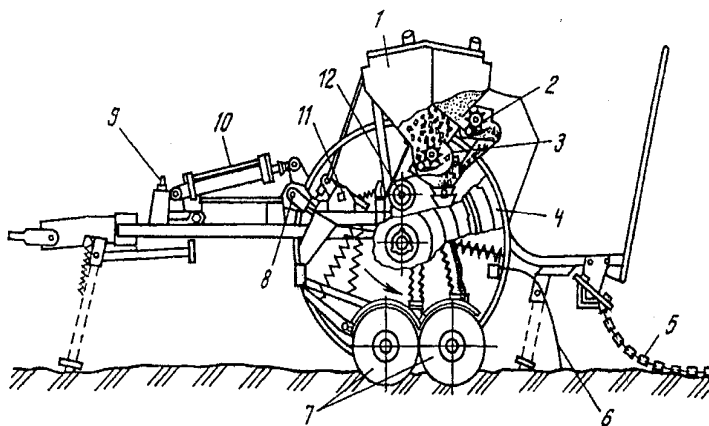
Сеялка СЗ-3,6А: 1 – зернотуковый ящик; 2 – туковысевающий аппарат; 3 – семявысевающий аппарат; 4 – колесо; 5 – шлейф; 6 – загортач; 7 – сошник; 8, 11 – круглый и квадратный валы; 9 – регулировочный винт; 10 – гидроцилиндр; 12 – контрприводной вал
